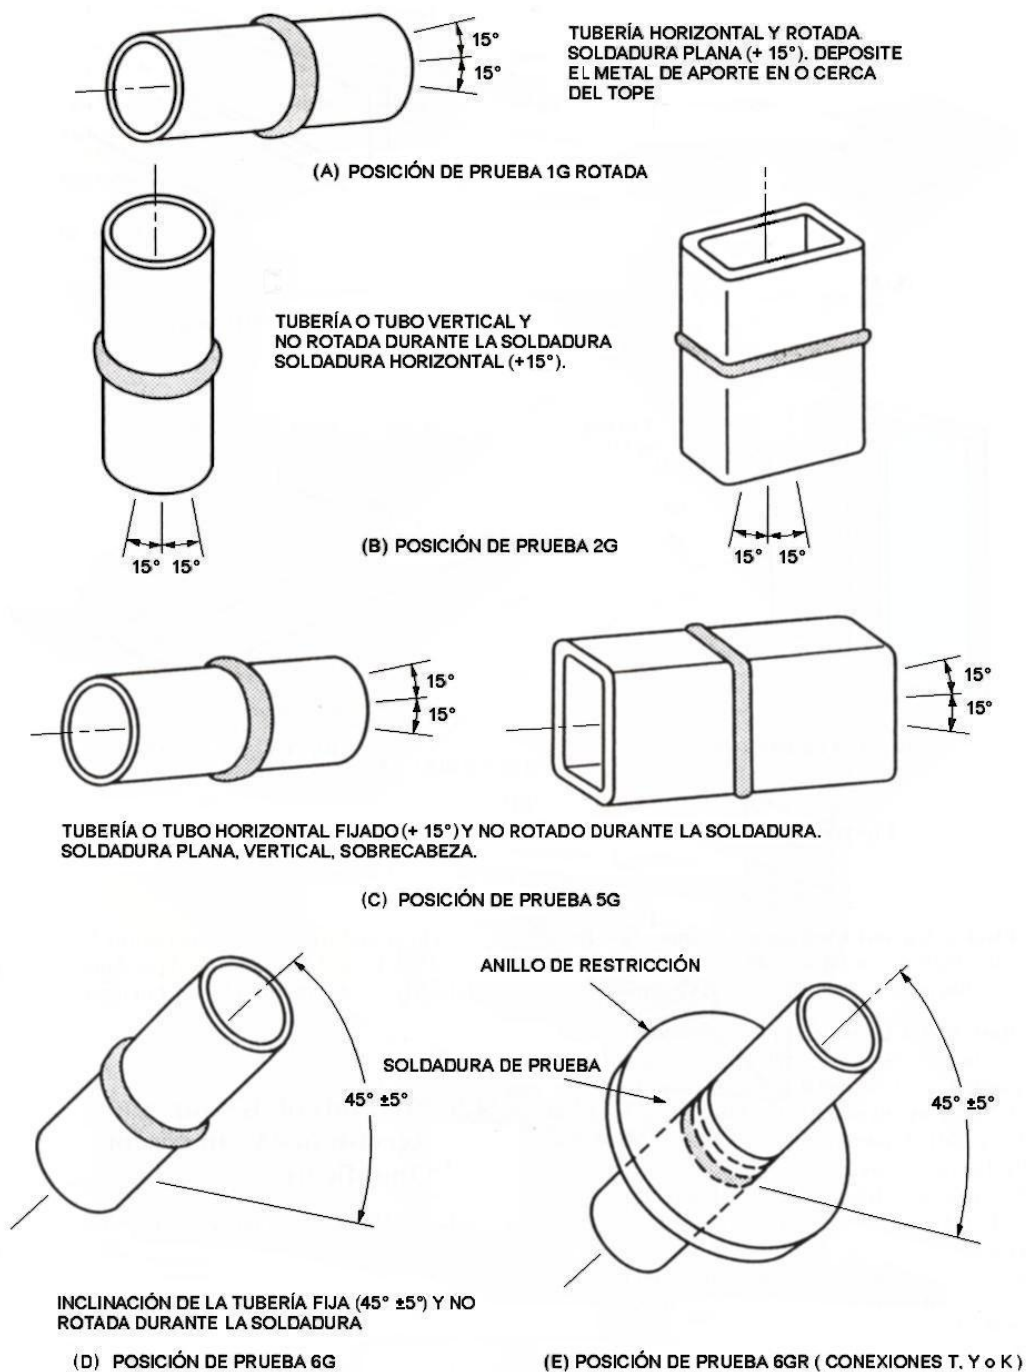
POSICIONES DE SOLDADURA DE RANURA EN TUBOS PARA CALIFICACIÓN (3)
